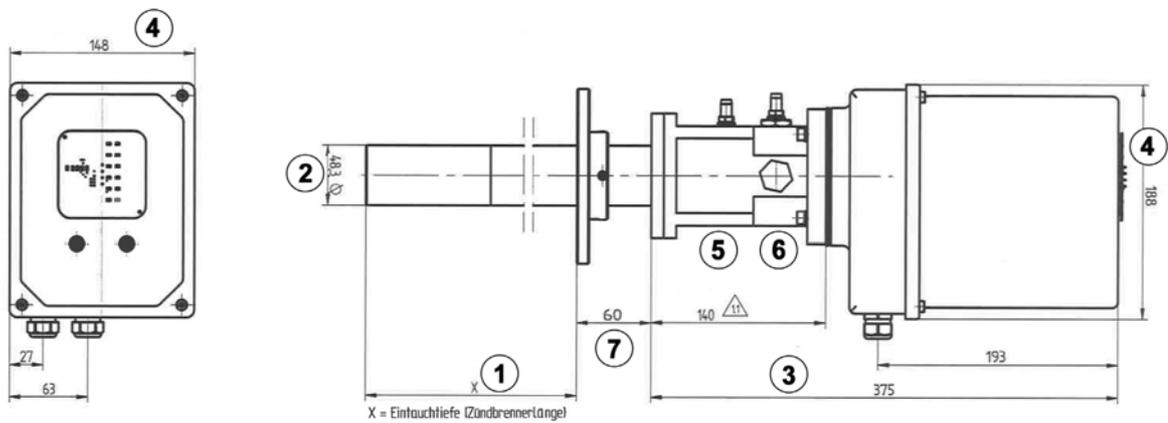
Dimensiones del quemador de ignición GFI48, variante A/B
